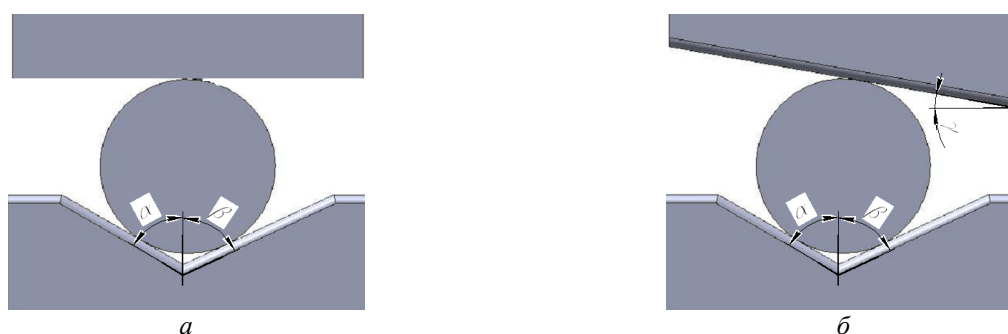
Схема протяжки цилиндрической заготовки комбинированными бойками (нижний боек вырезной несимметричный верхний плоский (а), скошенный (б))
